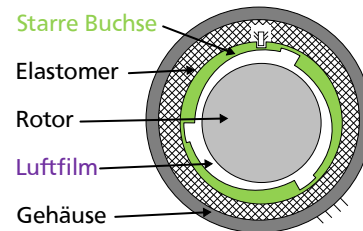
Air Ring Bearing mit einer Dreikeilinnenkontur der Buchse [1–3].
